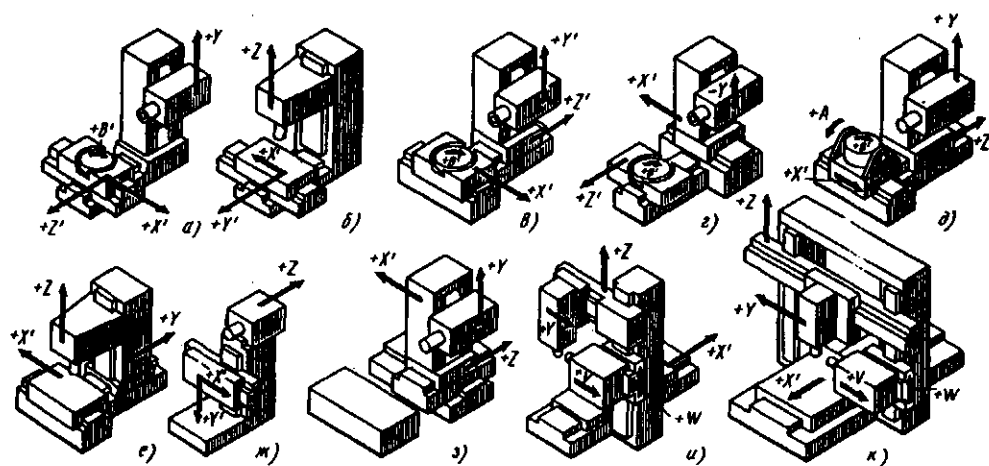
Основные (базовые) типы сверлильно-фрезерно-расточных станков
